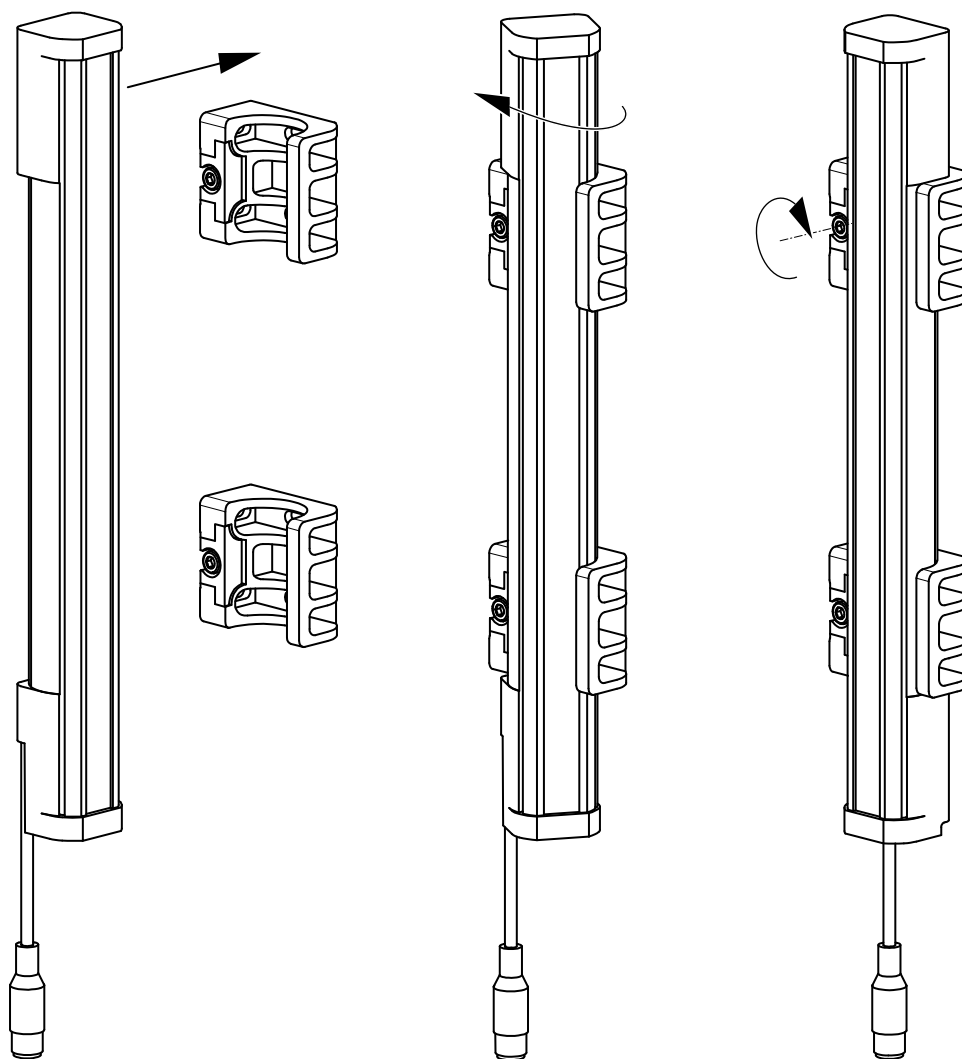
Установка многолучевого защитного светового барьера в крепления FlexFix
